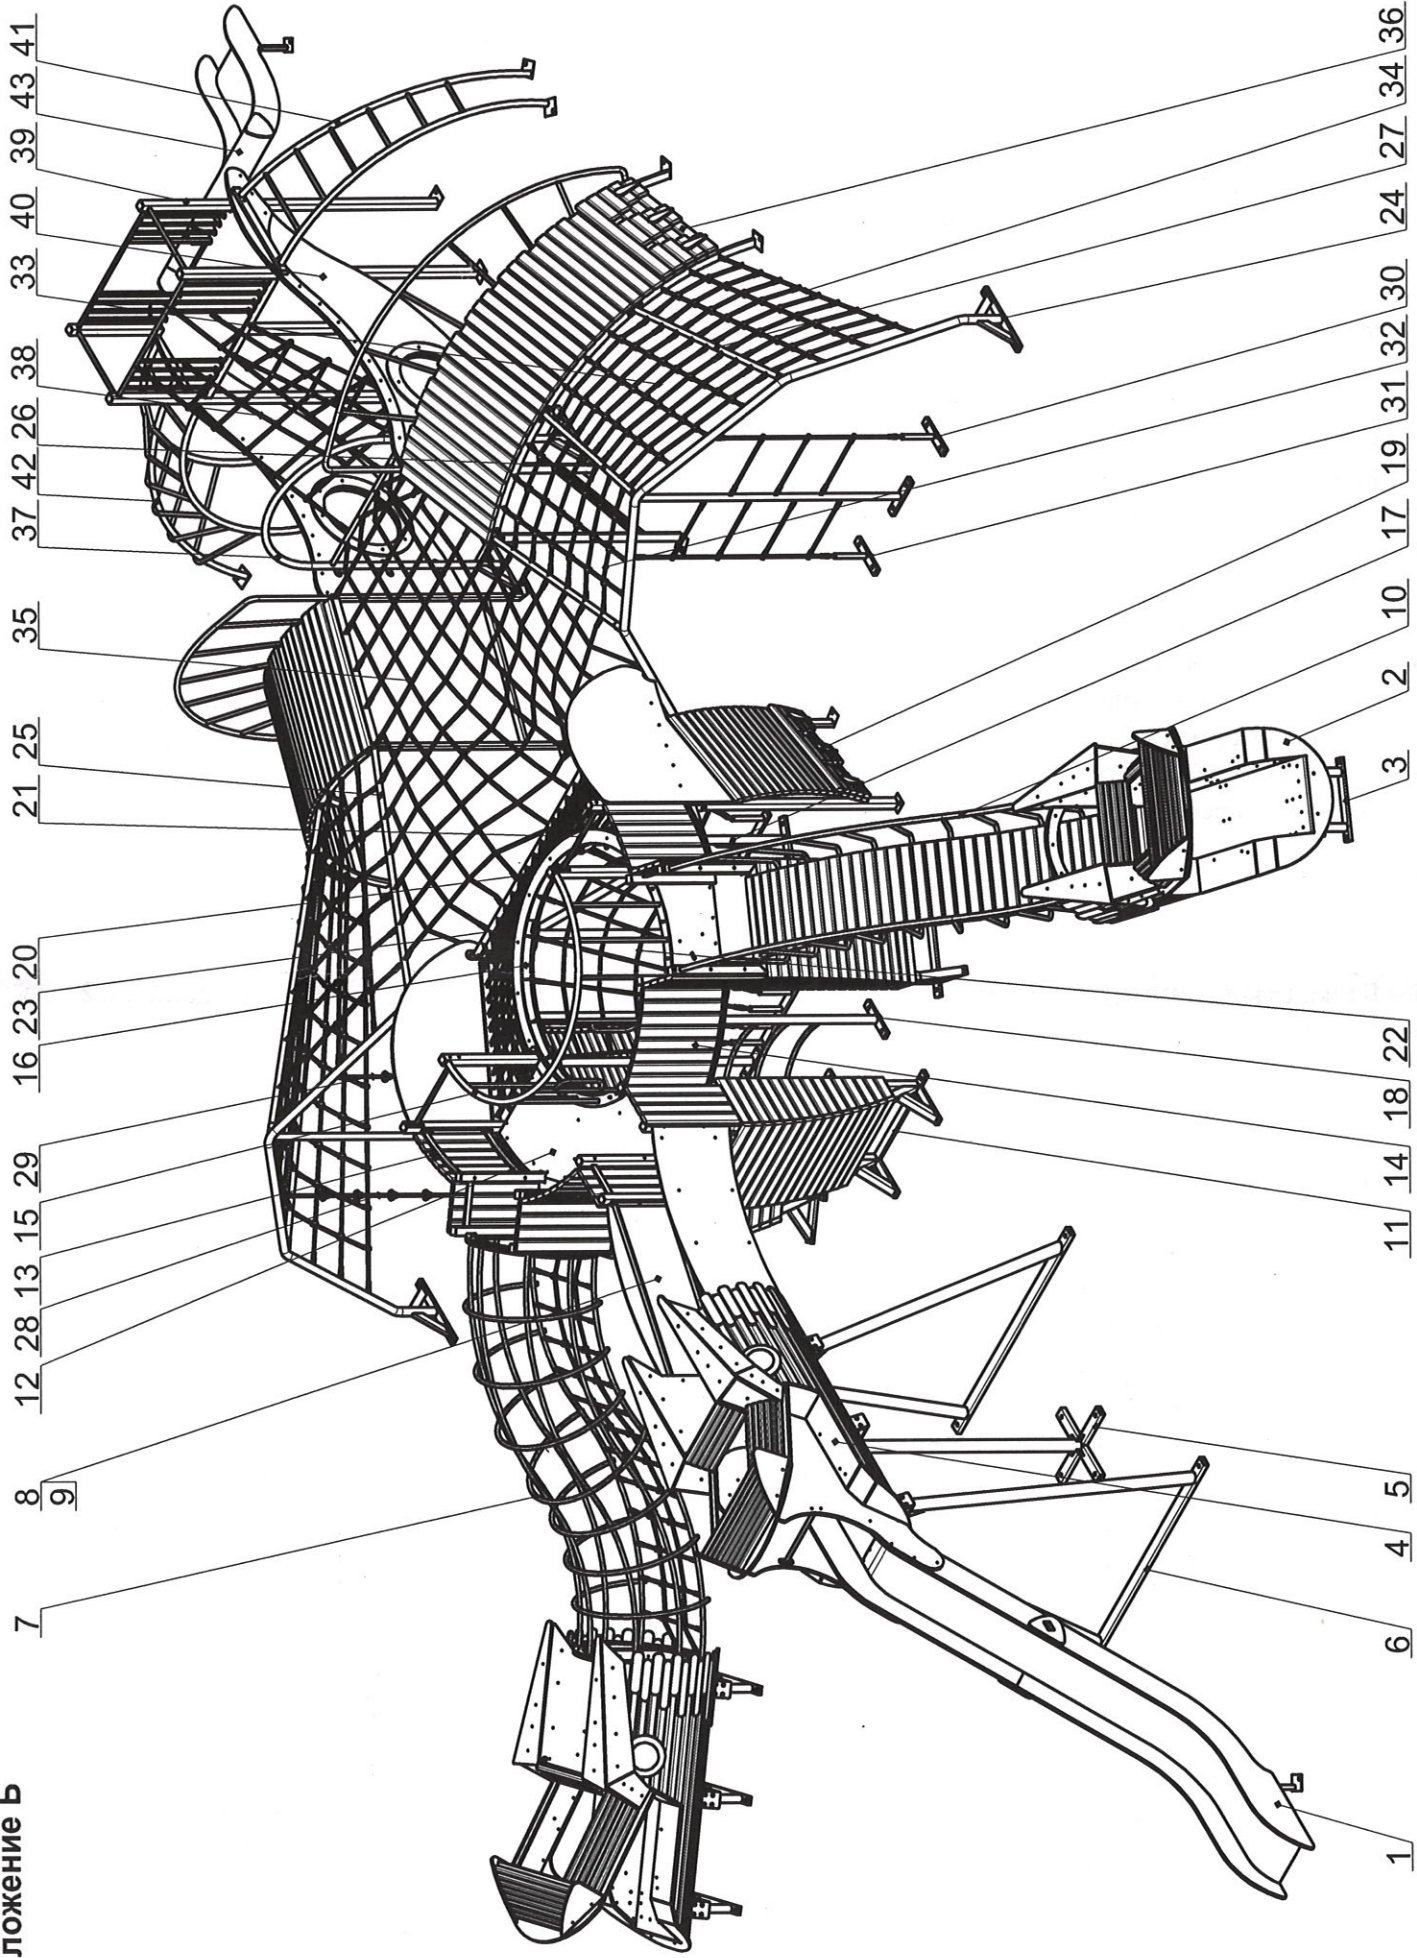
а - Общий вид изделия (изометрия) с обозначением позиций согласно комплектности
